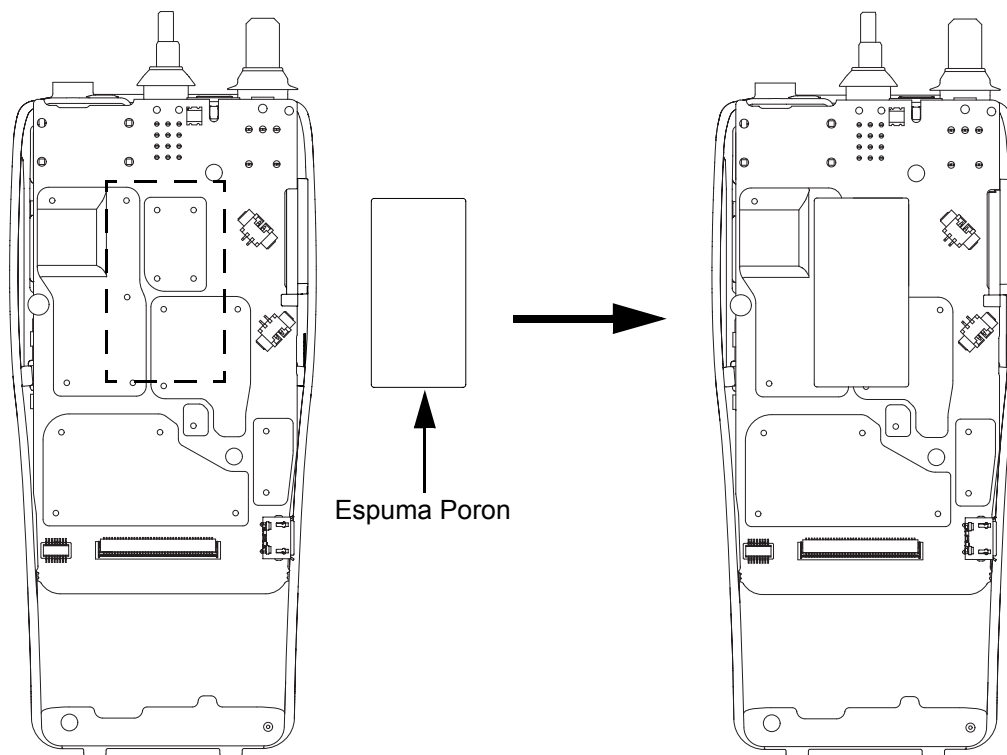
Montagem do PCB e da Vedação do controle superior
